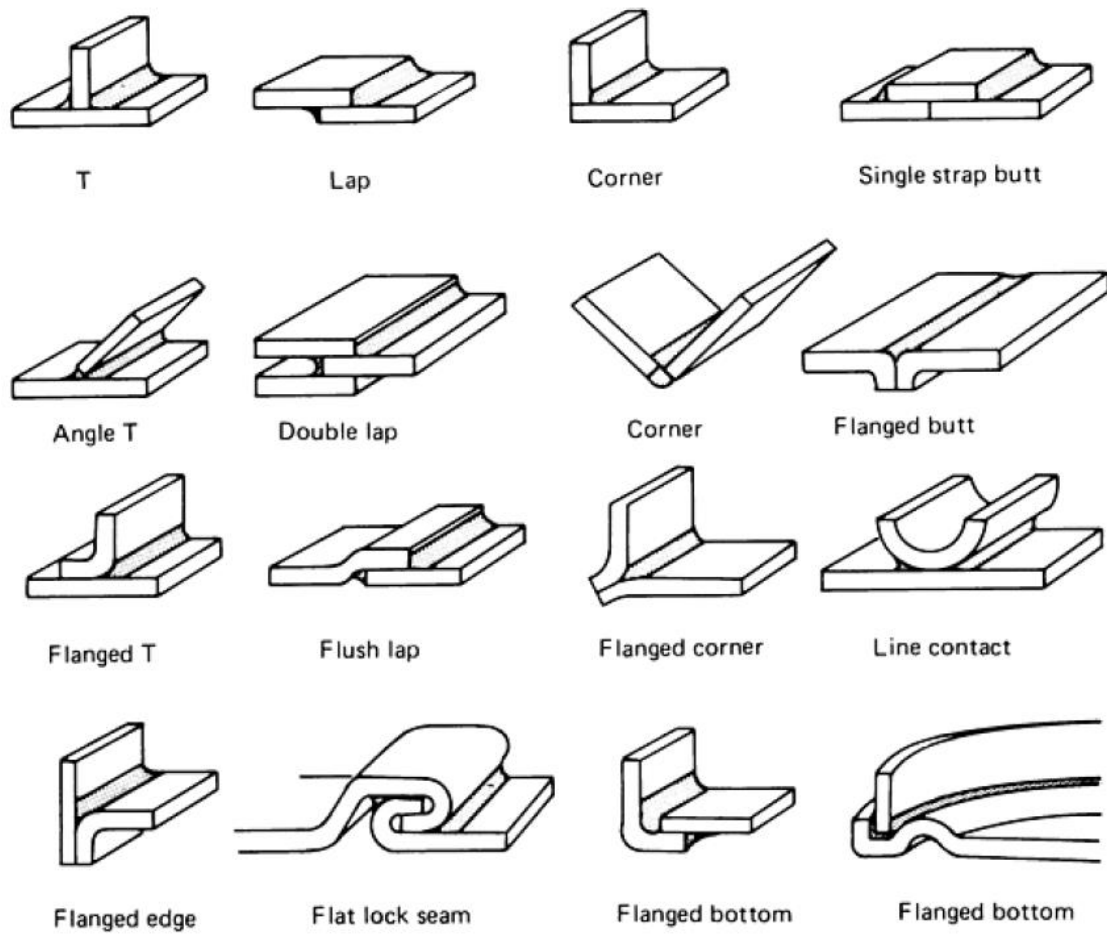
Juntas usualmente utilizadas em soldadura [4]
